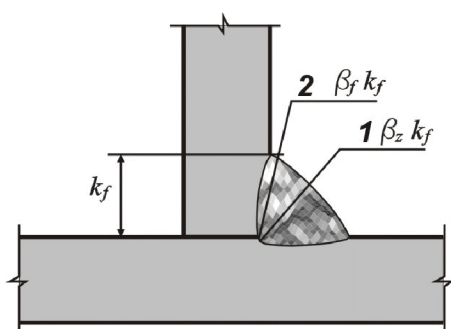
Схема расчетных сечений сварных соединений с угловыми швами.
